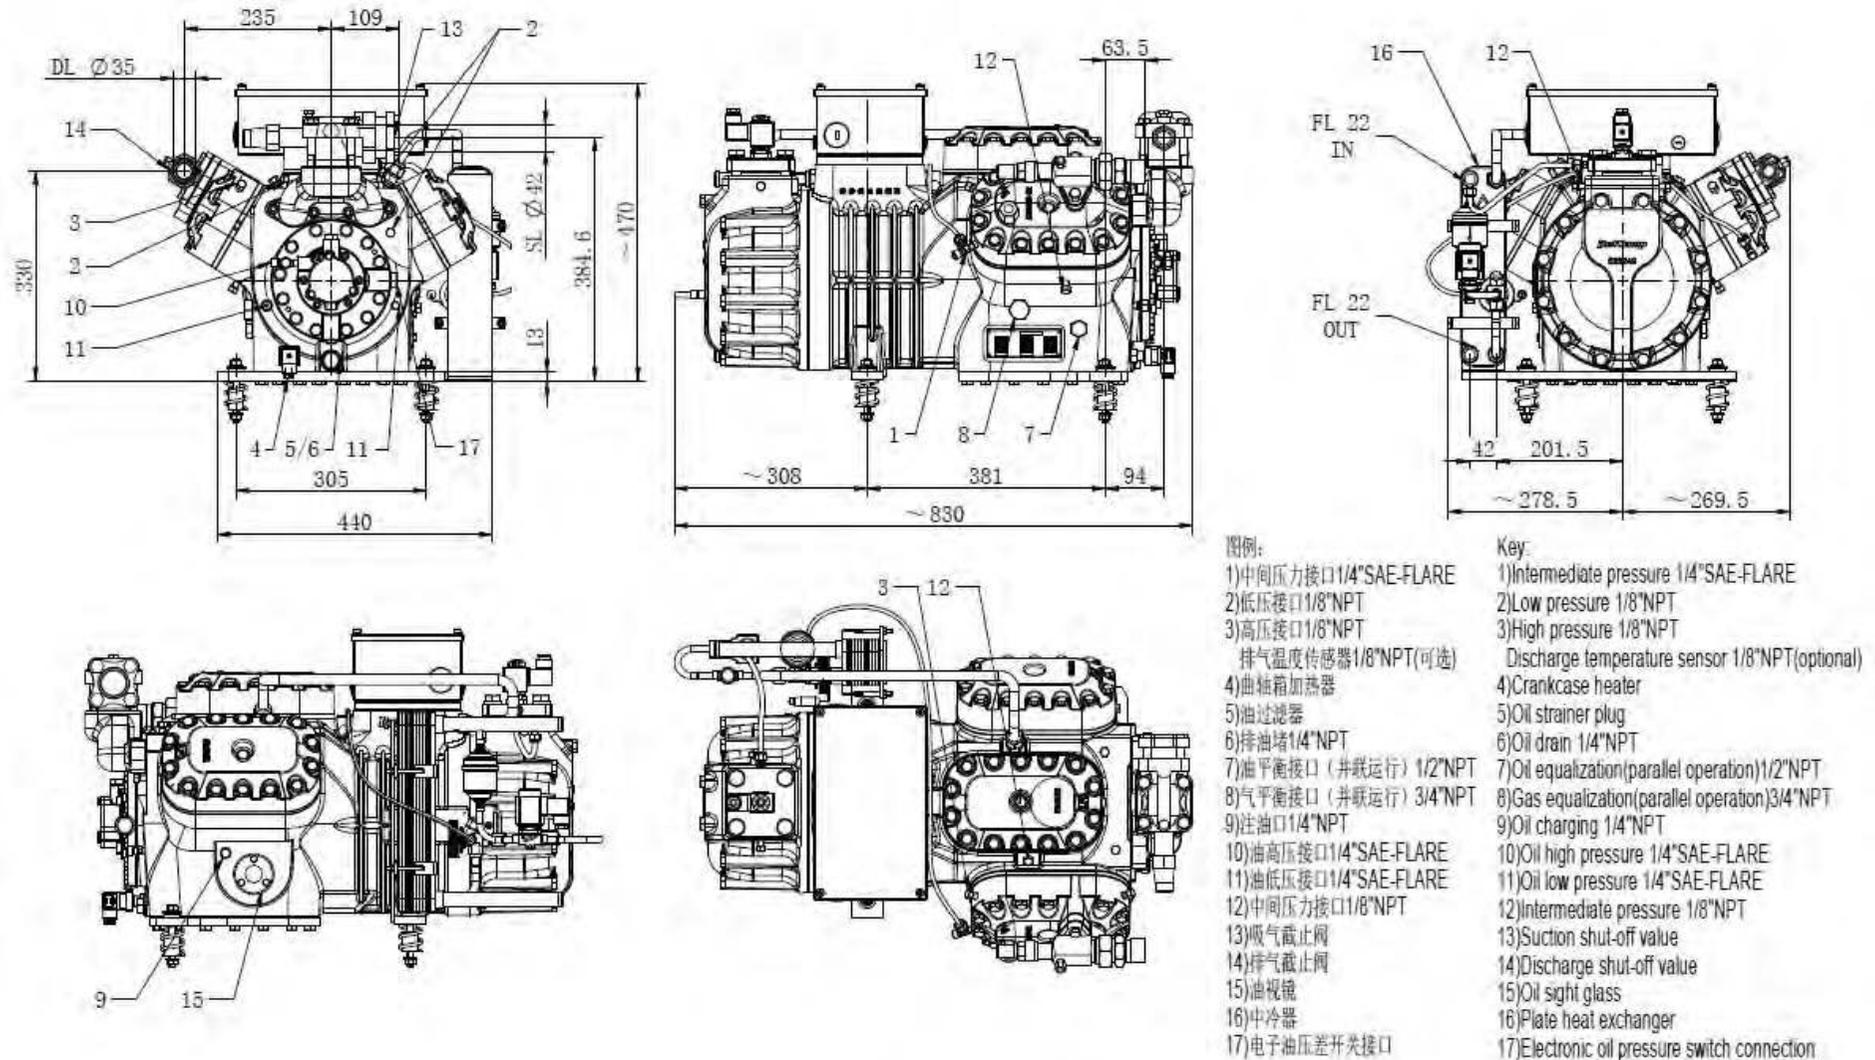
Габаритные размеры модели SB6C-1600~3000
